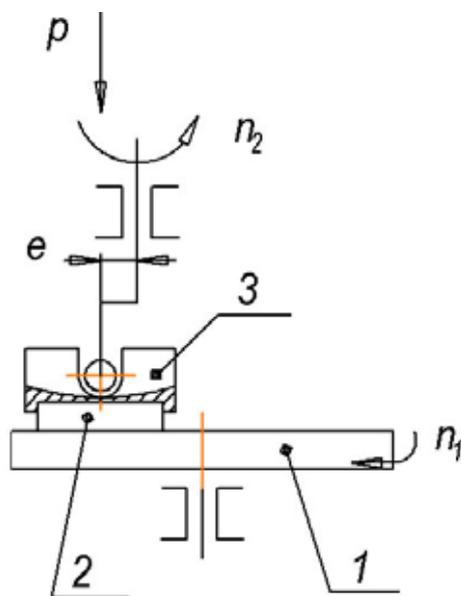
Схема притирки поверхностей: 1 – притир; 2 – заготовка; 3 – держатель заготовки; n_1 – частота вращения притира; e – радиус кривошипа механизма вращения заготовки; n_2 – частота вращения заготовки; P – усилие прижатия заготовки к притиру
